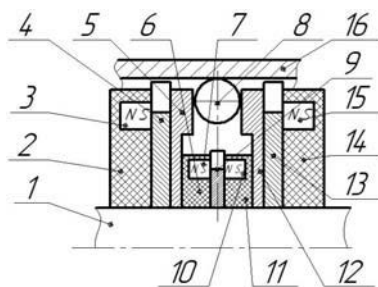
Схема магнитно-динамического раскатывания при комплексной обработке: 1 – оправка; 2 – обойма; 3 – источник магнитного поля; 4 – зубчатый магнитопровод; 5, 12 – диски; 6, 11 – обоймы магнитной системы разгона; 9 – зубчатый магнитопровод магнитной системы разгона; 7, 10 – источники магнитного поля; 8 – деформирующие шары; 13 – зубчатый магнитопровод; 14 – обойма; 15 – источник магнитного поля; 16 – обрабатываемая заготовка
